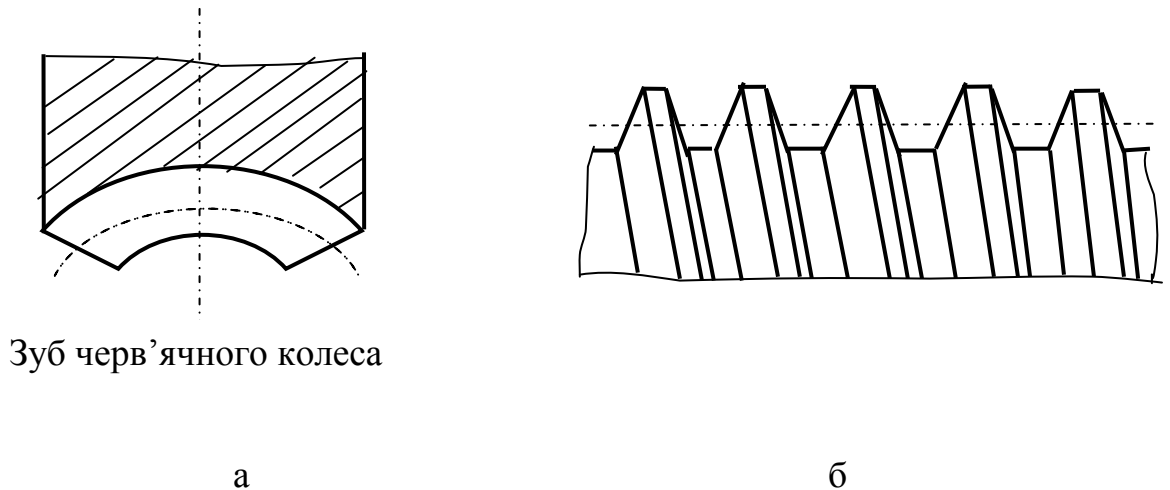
Вигляд зубця черв'ячного колеса (а) та зубців черв'яка (б)
